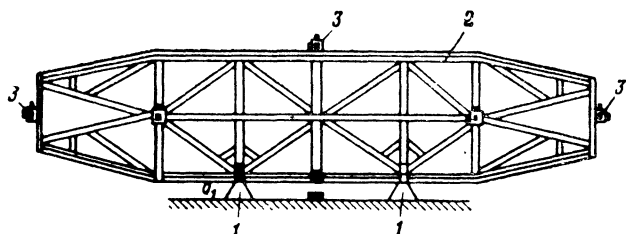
Схема конструкции сварного трубчатого каркаса рефлектора:
